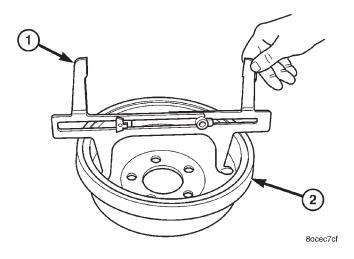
CALIBRADOR DE AJUSTE EN EL TAMBOR
